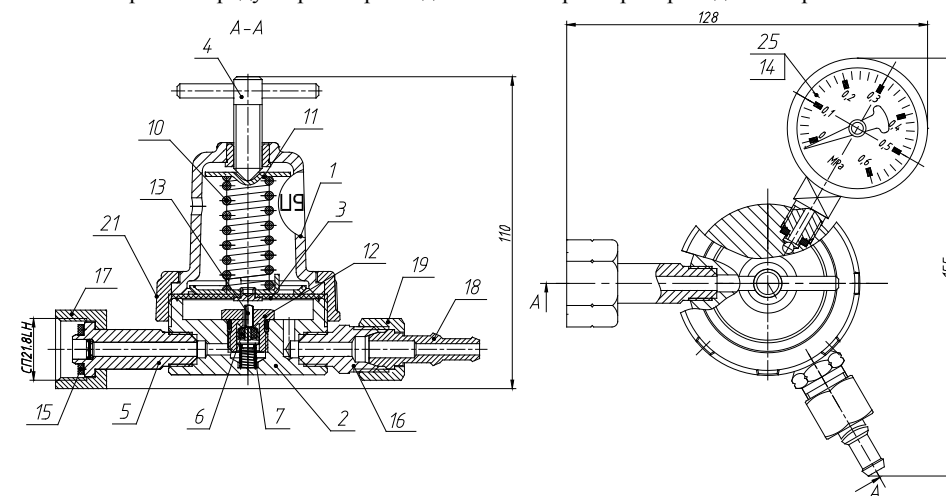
Редуктор баллонный пропановый одноступенчатый.
